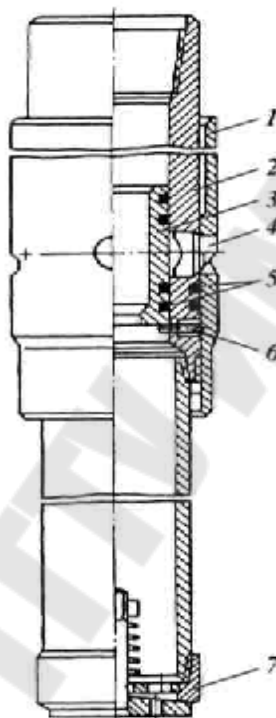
Замковый разъединитель: 1 – муфта; 2 – ниппель; 3 – запорная втулка; 4 – замок; 5 – уплотнения; 6 – срезной штифт; 7 – обратный клапан
